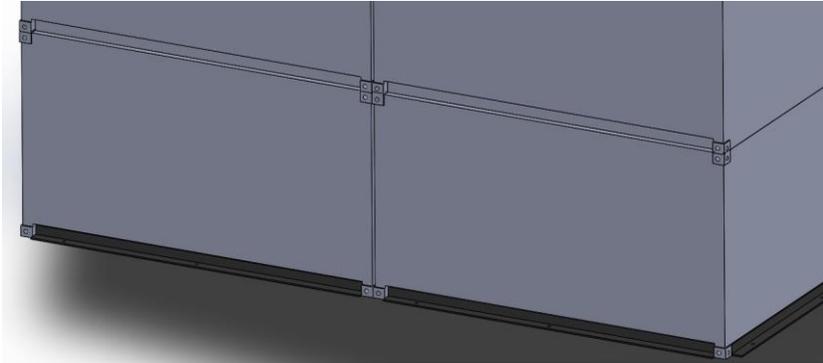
Disposición de las guías en la base de la estructura (Elaboración propia)
